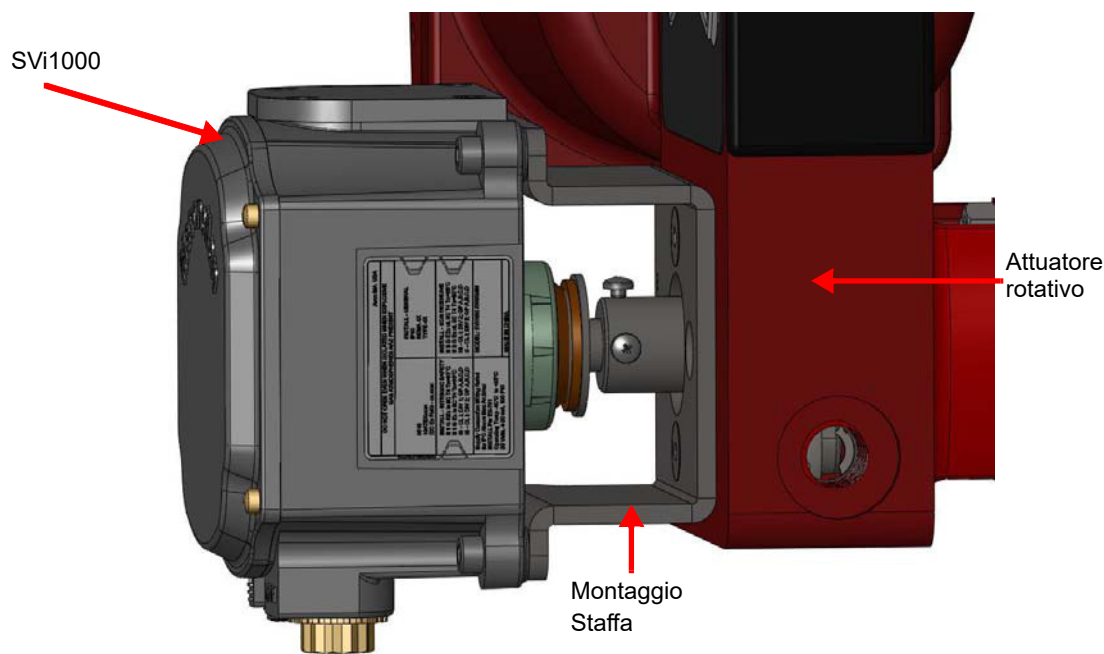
Camflex con staffa di montaggio (vista laterale)
